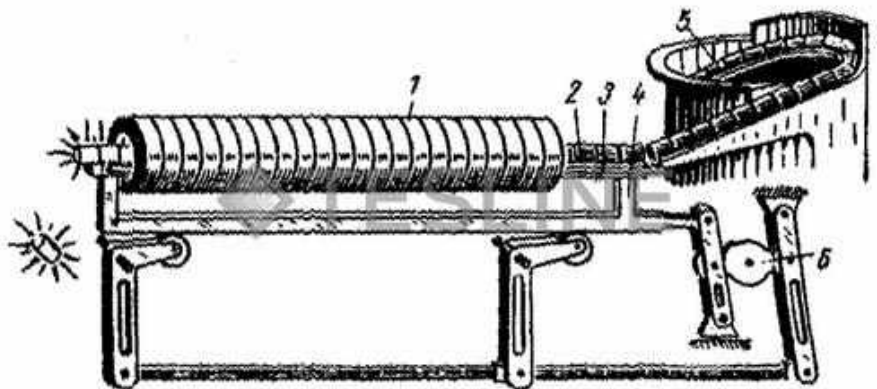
Схема методического нагревателя с цилиндрическим индуктором и шагающим механизмом для транспортирования заготовок:
